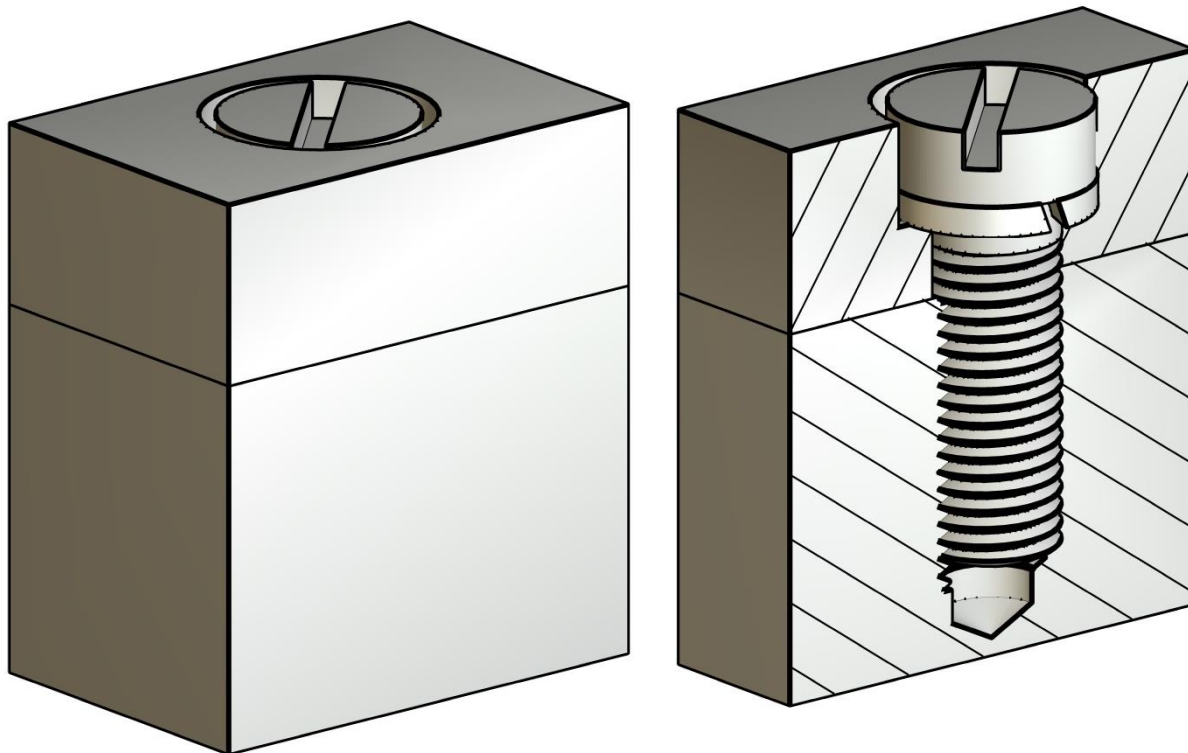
Соединение деталей стандартными крепежными изделиями – винтом с цилиндрической головкой (ГОСТ 1491-80) и пружинной шайбой (ГОСТ 6402-70), удерживающей винт от самопроизвольного вывинчивания (справа изображение выполнено условно в разрезе)
